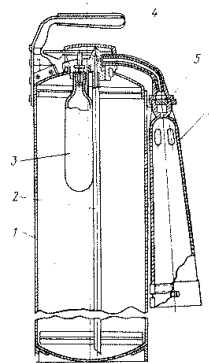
Повітряно-пінний вогнегасник ОВП-10 1 - корпус; 2 - сифонова трубка; 3 - балон; 4 - рукоятка; 5 - розпилювач; 6 - розтруб з сіткою
